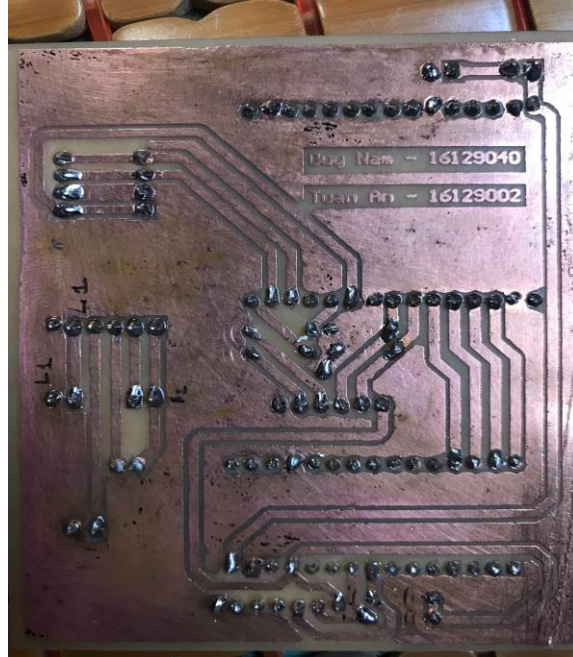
Sơ đồ mạch PCB của thiết bị
